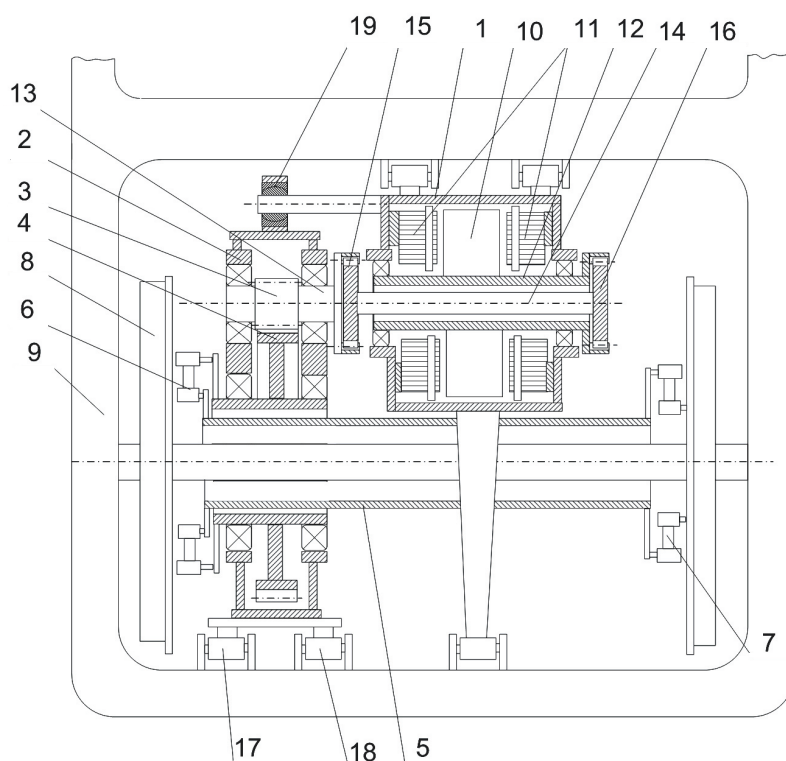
Агрегатная схема компоновки тягового привода с полностью обрессоренными массами:
